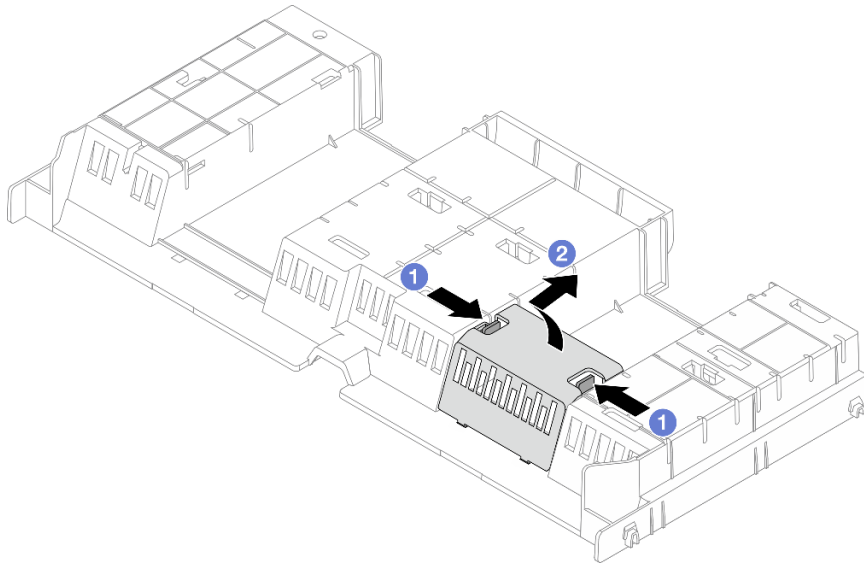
Entfernen der Abdeckblende der Luftführung
